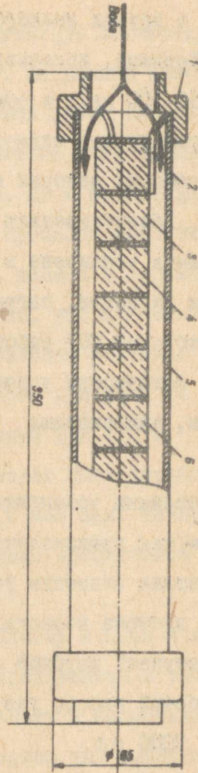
Магнитный водообрабатывающий прибор с постоянным магнитом. 1 - соединительная муфта; 2 - центральный штифт; 3 - постоянный магнит; 4 - промежуточная шайба; 5 - наружный кожух; 6 - внутренний кожух.
